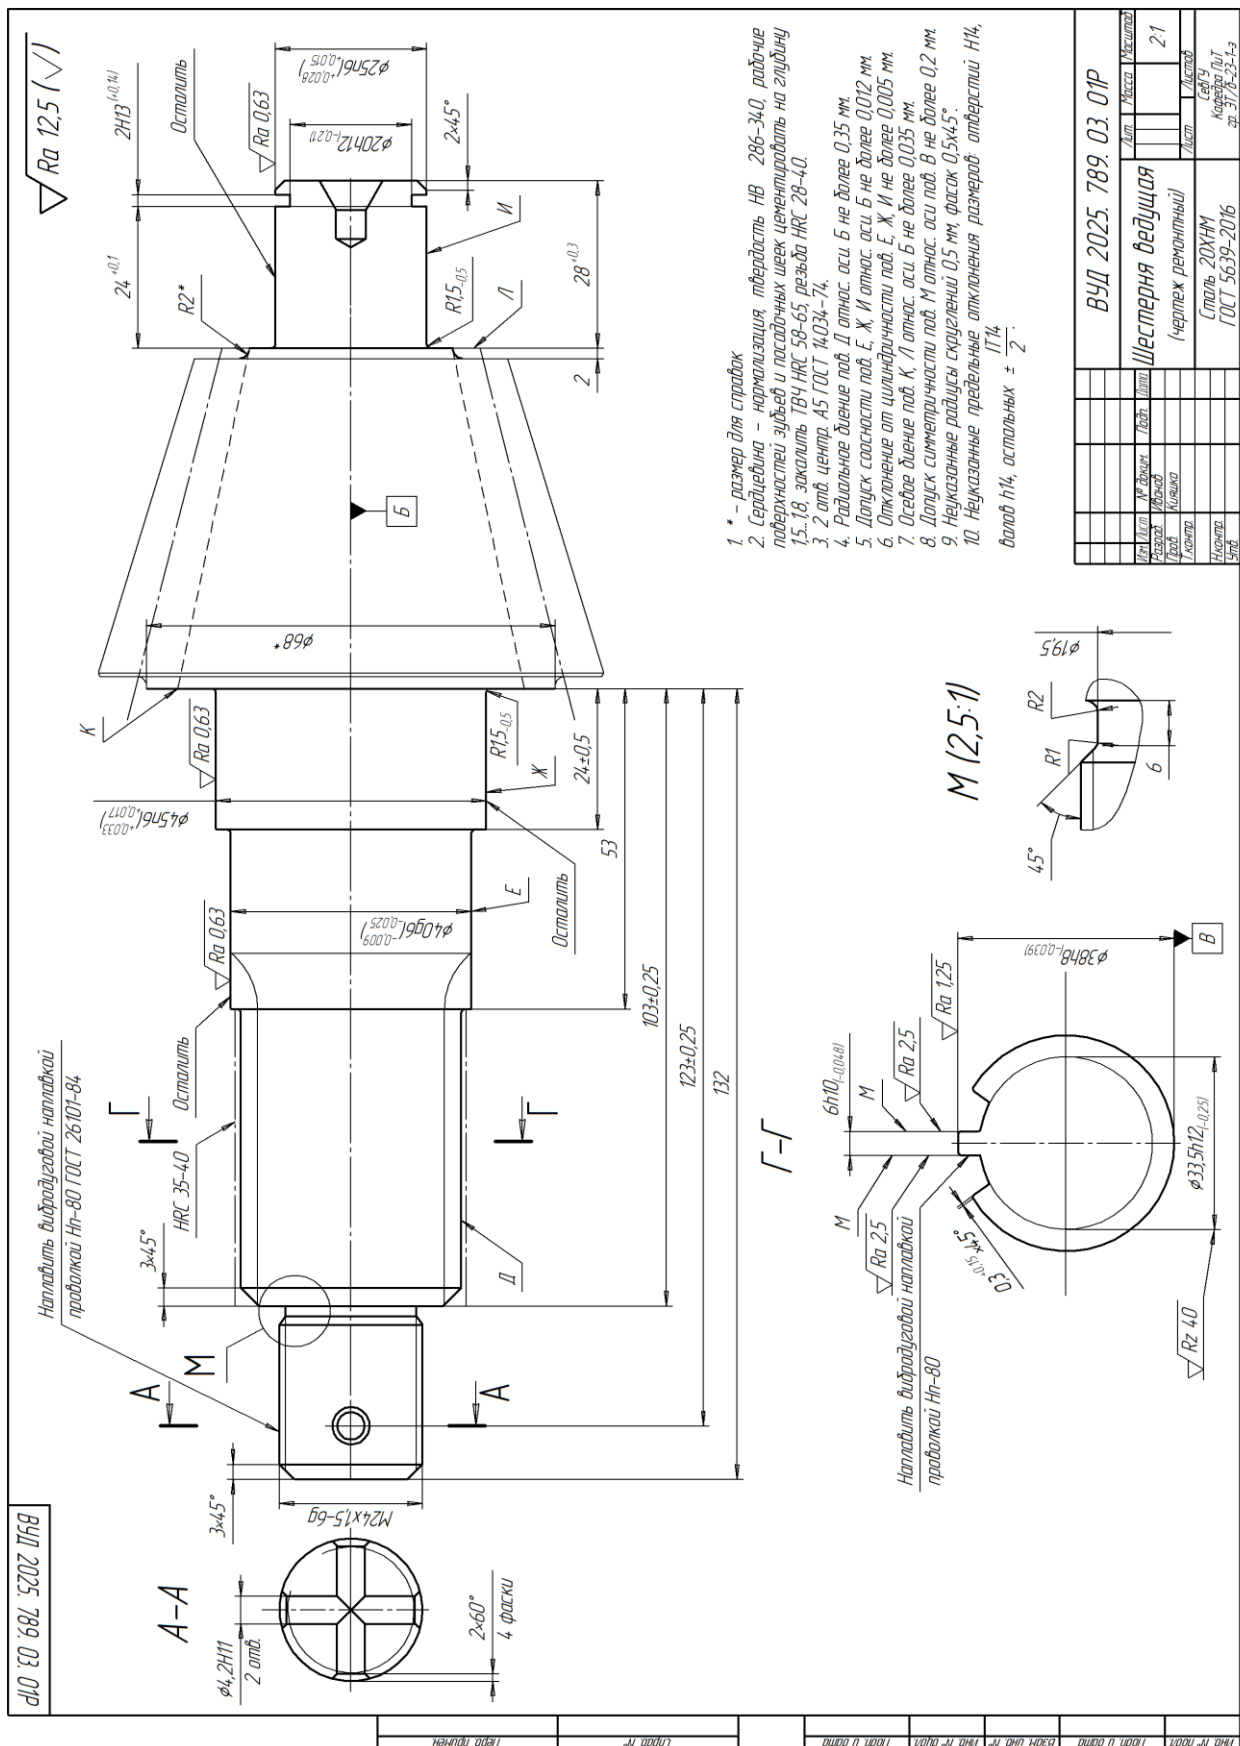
Ремонтный чертеж ведущей шестерни главной передачи
